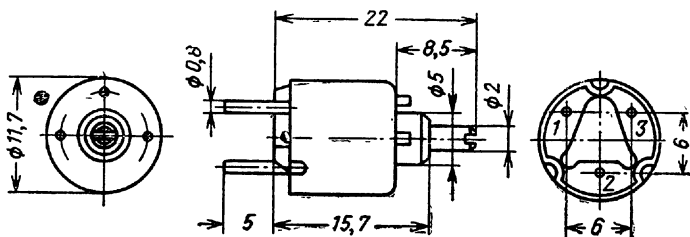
Общий вид резисторов СПЗ-6А.
